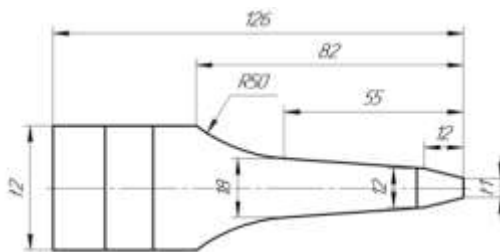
Профиль поперечного сечения ультразвукового сварочного инструмента
